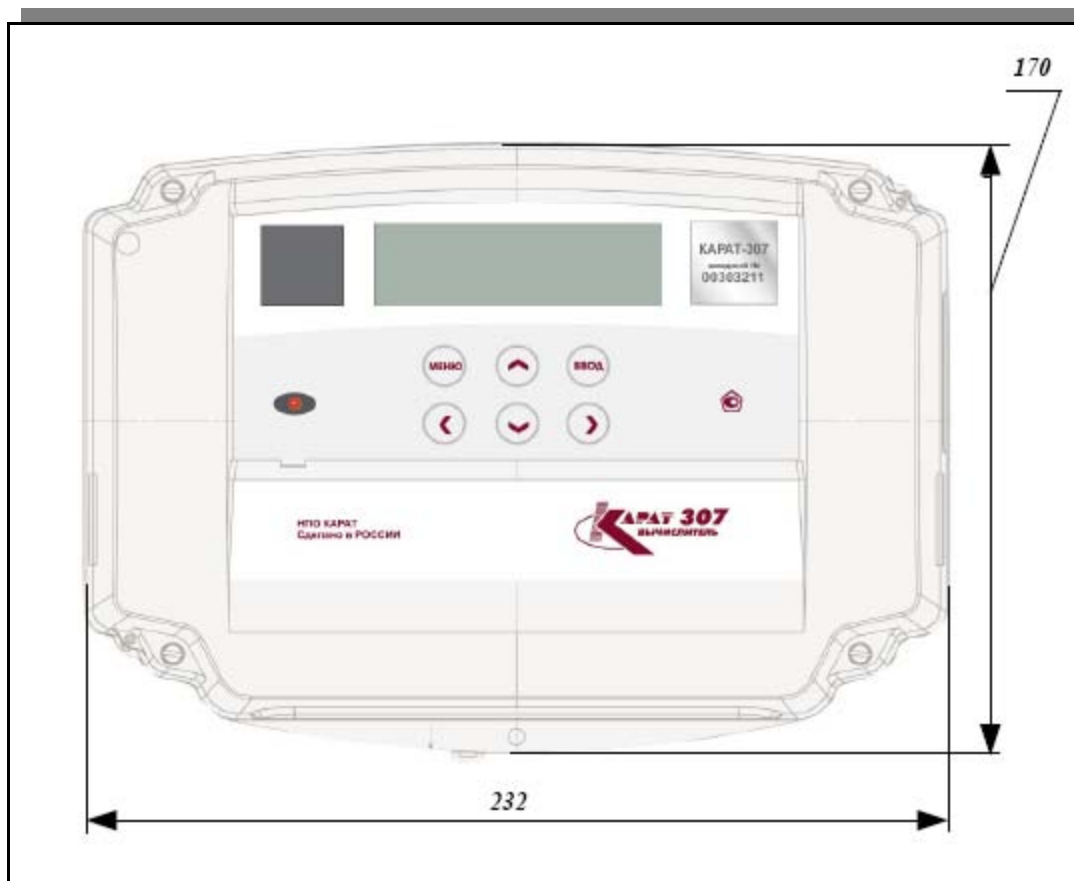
Габаритные размеры вычислителя KARAT-307
